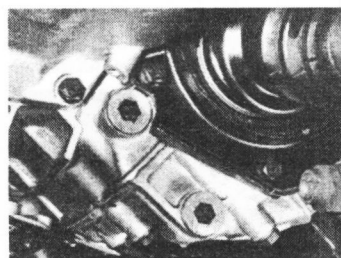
Заглушки горловины и сливного отверстия конечного привода
